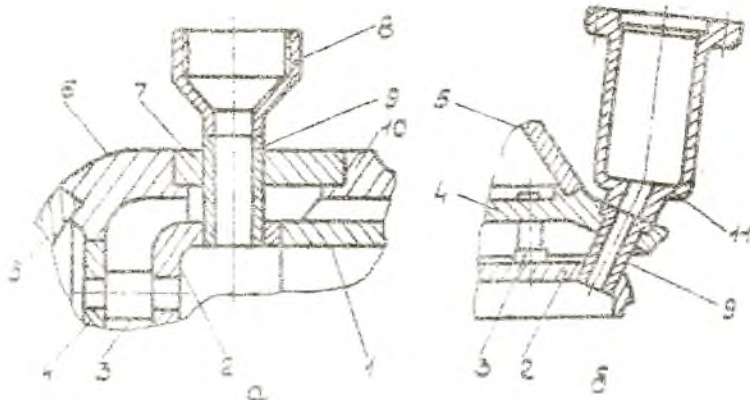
Схемы установки воспламенителя: а – на кольце, соединяющем смесительную головку с корпусом; б – на корпусе смесительной головки; 1 – стенка корпуса камеры; 2 – внутреннее днище; 3 – форсунка; 4 – среднее днище; 5 – наружное днище; 6 – корпус головки; 7 – соединительное кольцо; 8 – штуцер для установки пиросвечи; 9 – переходная втулка; 10 – корпус камеры; 11 – корпус пиросвечи
